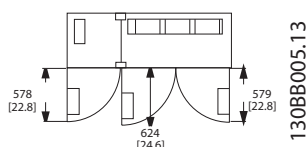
Пространство перед корпусом типа IP21/IP54, типоразмер F2.
